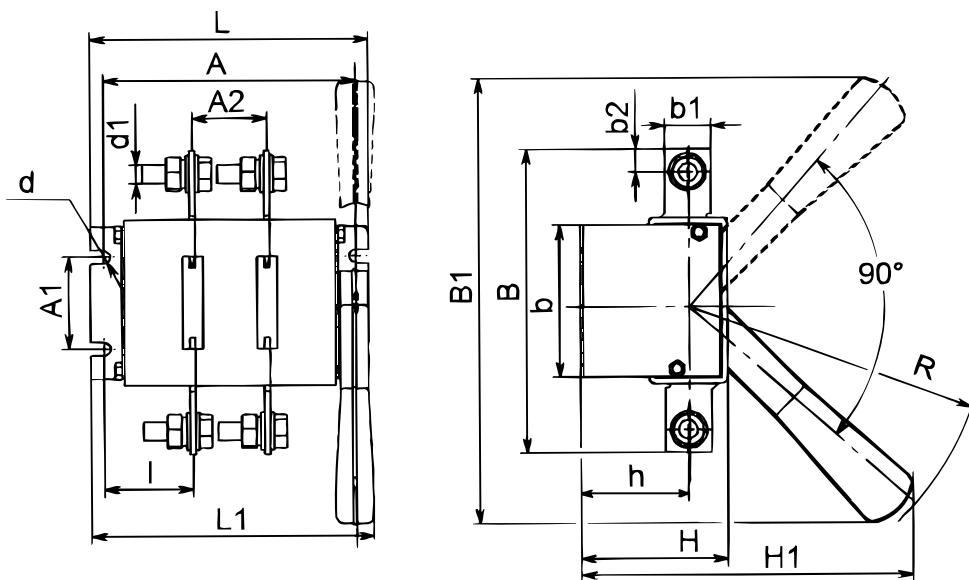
Выключатель-разъединитель на одно направление двухполюсный с боковой рукояткой
